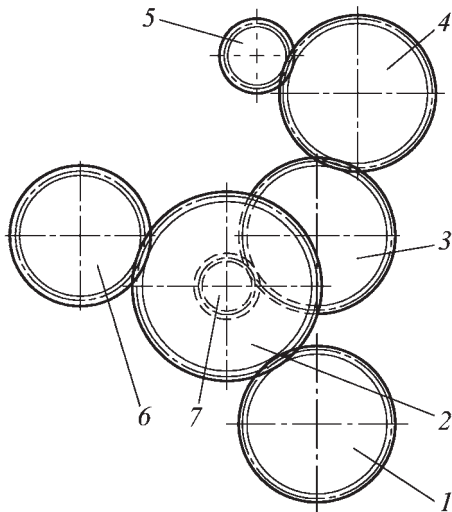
Схема механизма привода агрегатов двигателей семейства ЯМЗ-840:
